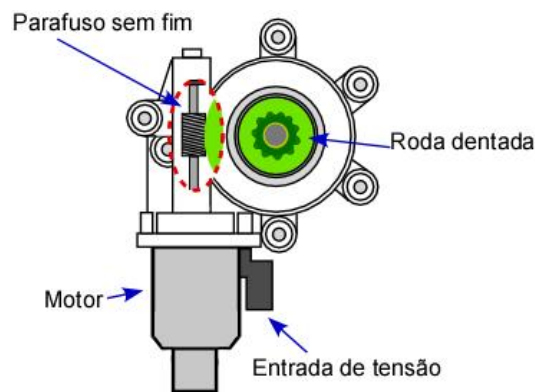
17 – Esquema do motor utilizado com pormenor da ligação do motor à roda dentada que faz a transmissão do movimento.
